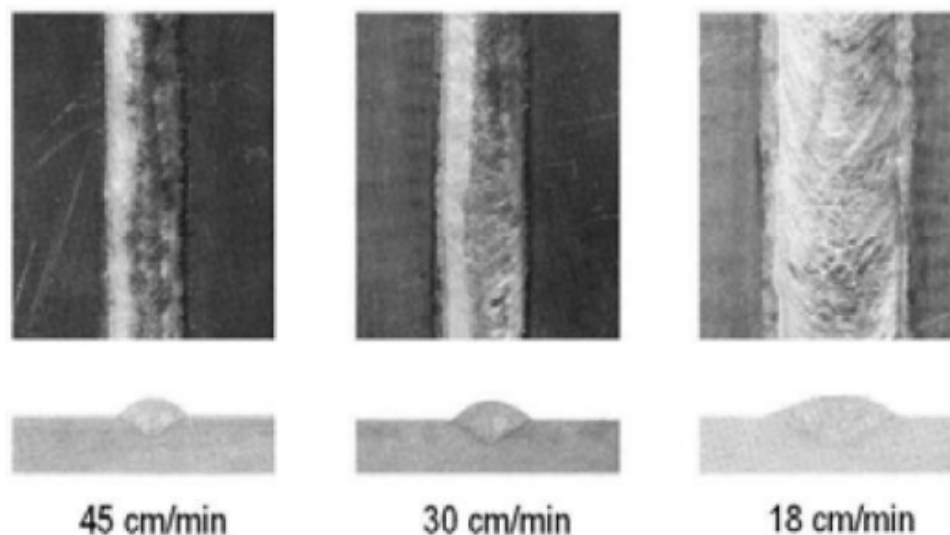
Efeito da velocidade de soldadura na penetração da solda – alumínio, aerosol, árgon [13].
